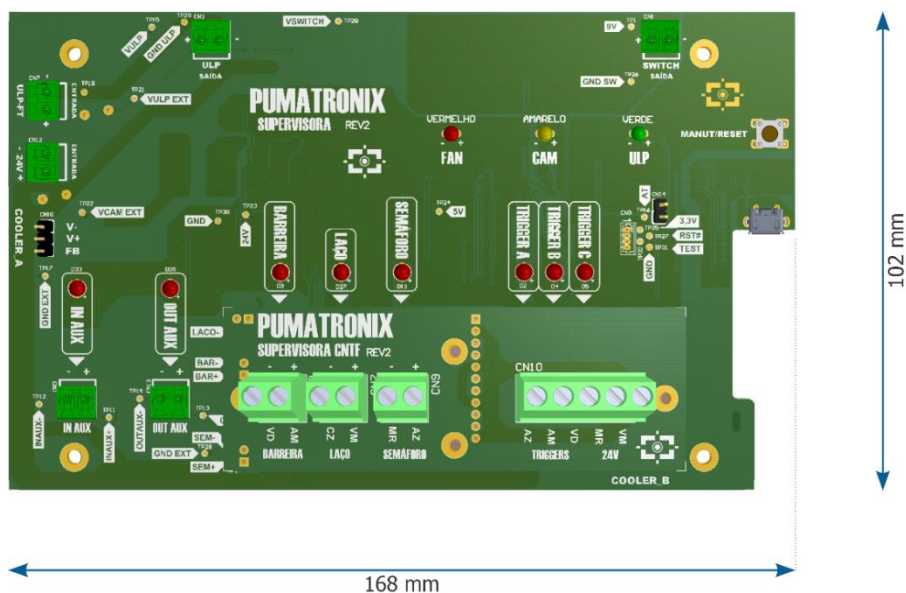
Dimensiones de la Placa Supervisora Rev2
